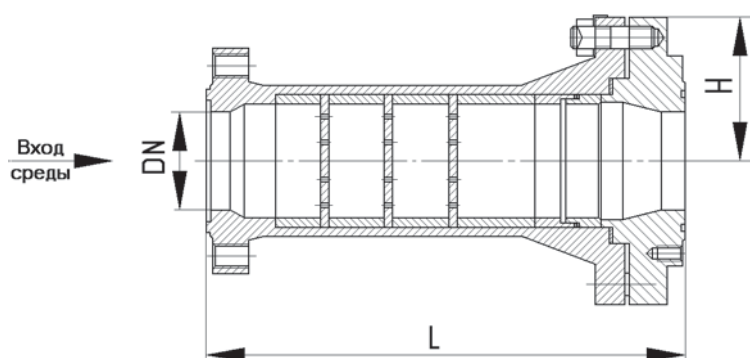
Клапан дроссельный проходной фланцевый
